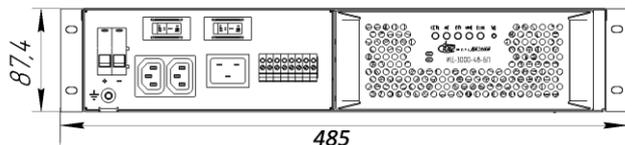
Габаритный чертеж ИЦ-1500-24-БП-19, ИЦ-3000-48-БП-19, ИЦ-3000-60-БП-19
